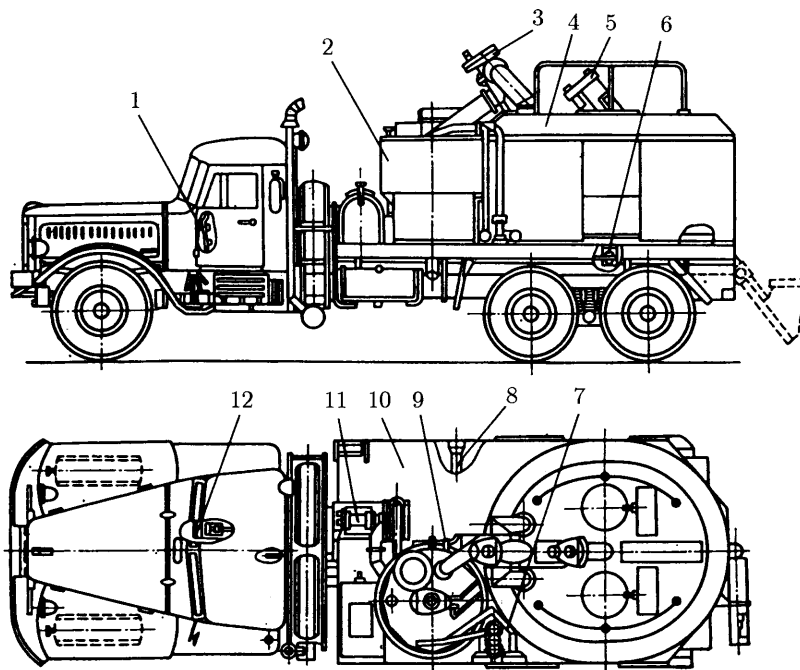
Агрегат 4ПА: 1 – пульт управления; 2 – аккумулятор; 3 – рабочий шнек; 4 – сварной бункер; 5 – загрузочный шнек; 6 – пневмовибратор; 7, 8 – соответственно приемный и раздаточный коллекторы; 9 – регулятор выдачи сыпучего материала; 10 – рама автошасси КрАЗ-257; 11 – центробежный песковый насос 5ПС-10; 12 – гидросистема.
